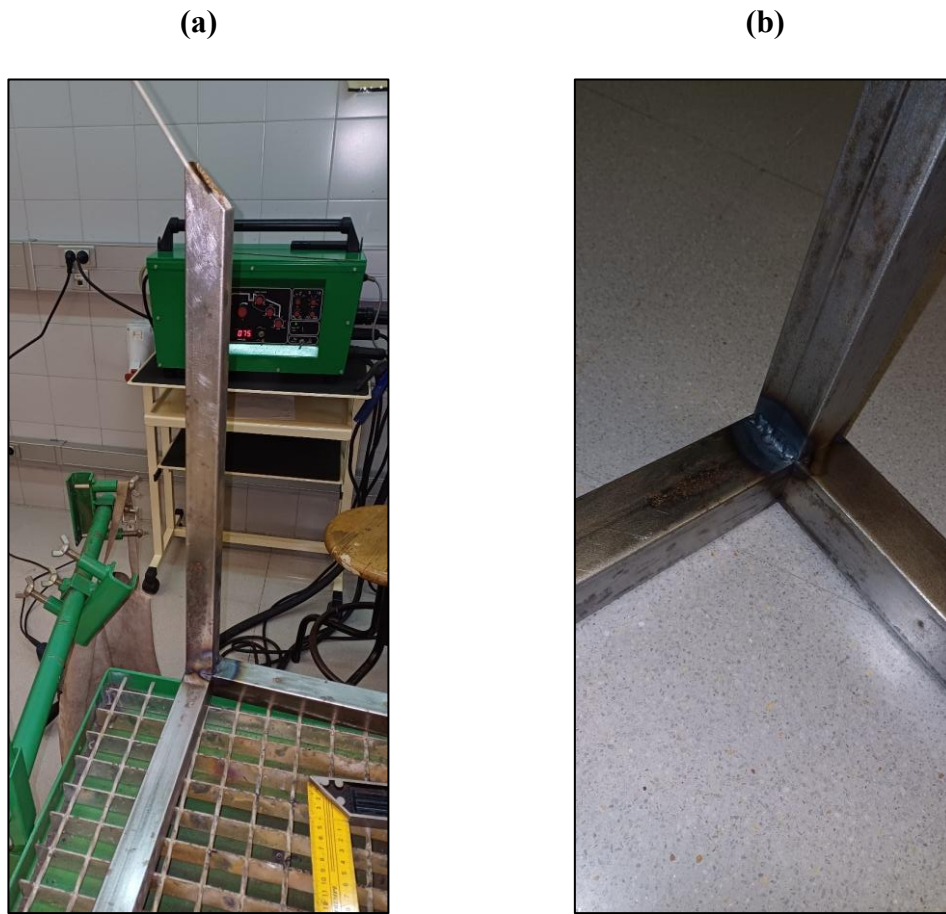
(a) Soldadura de perfil vertical, (b) Soldadura interior.
